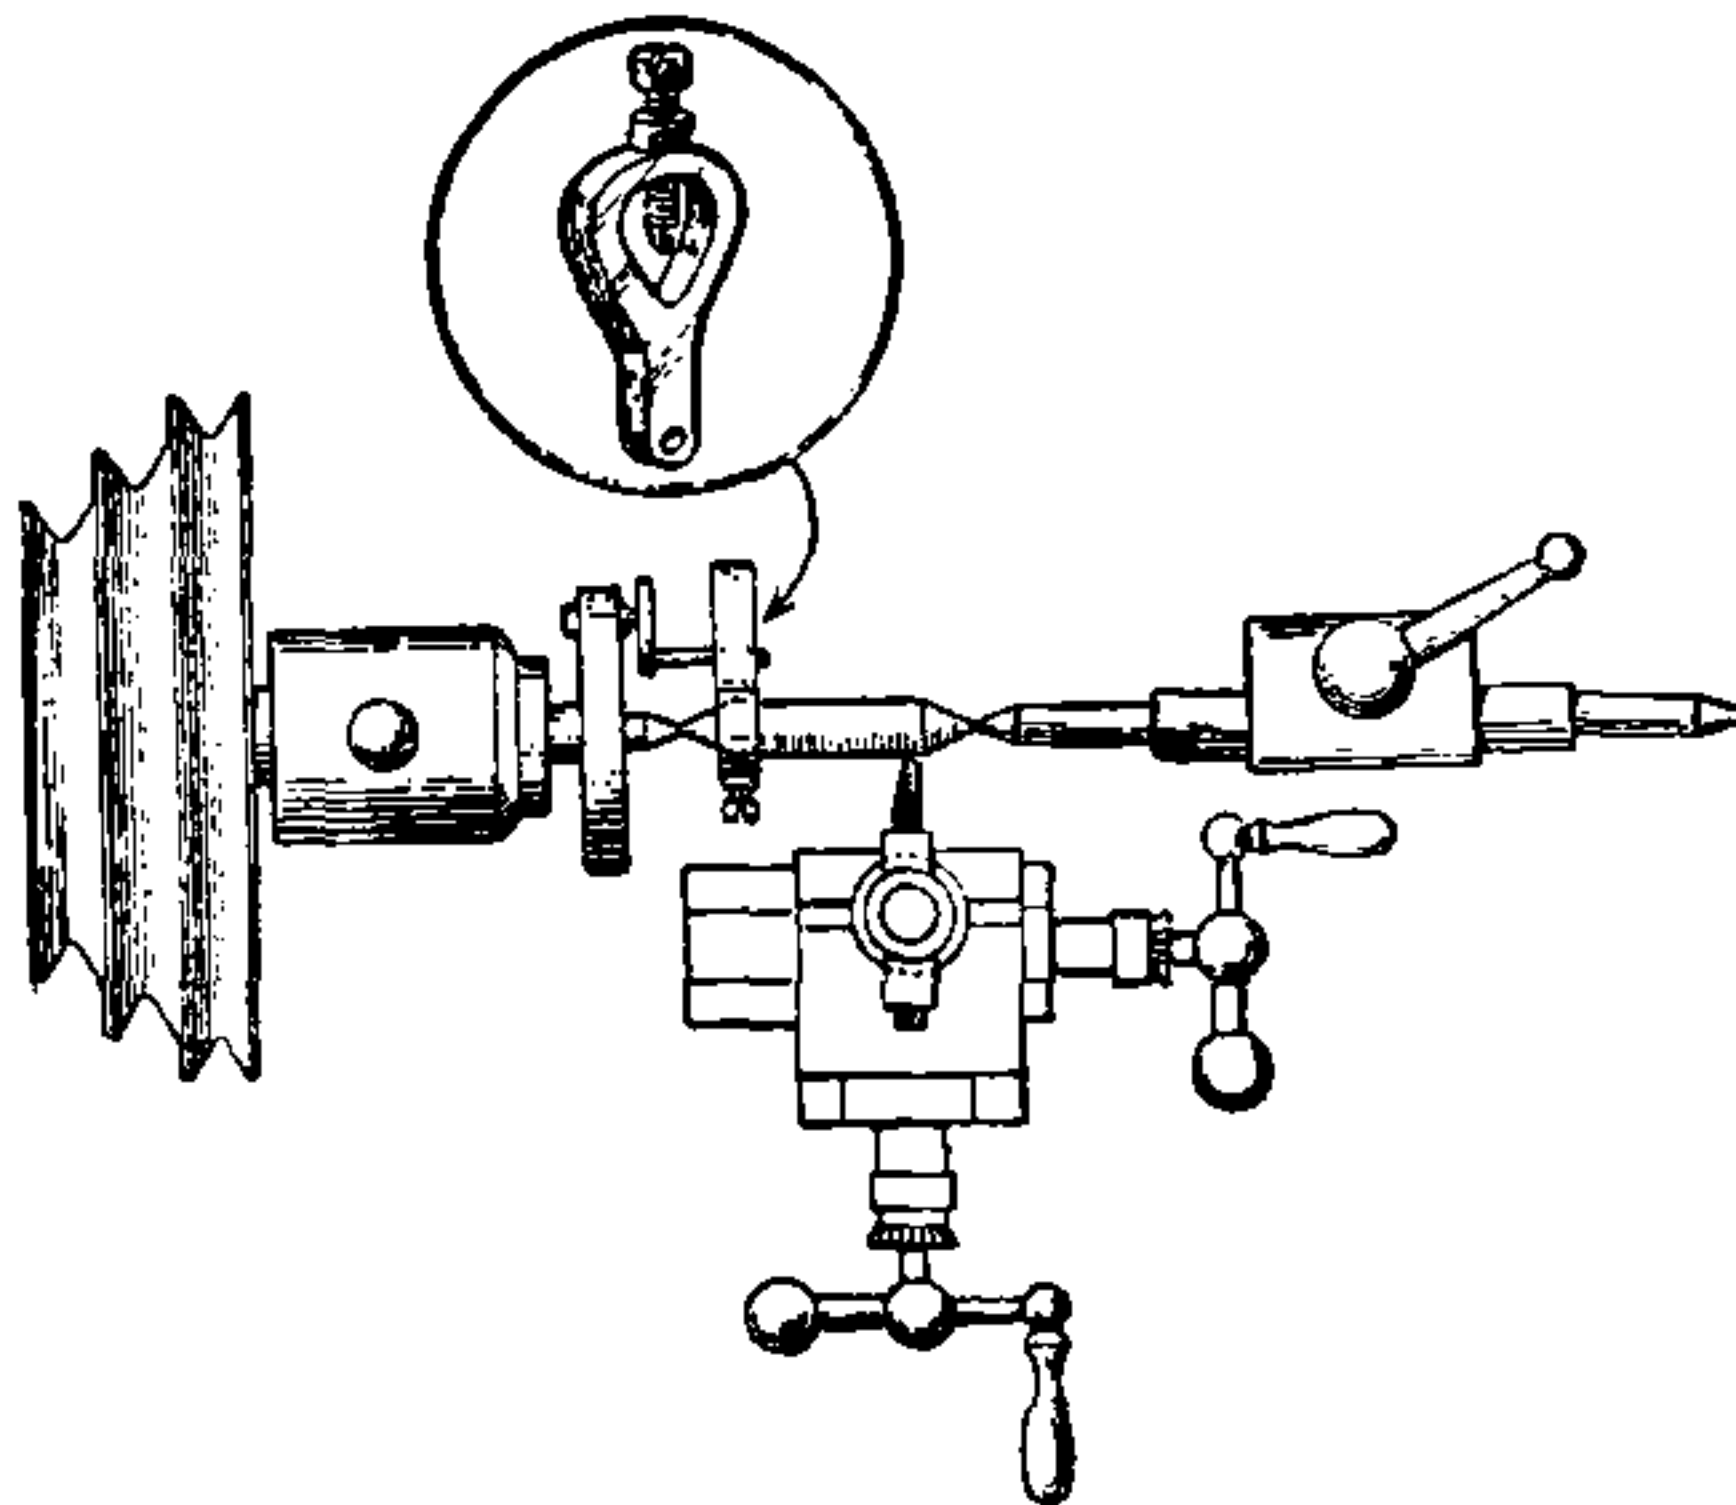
Montaggio per tornire col carrello un pezzo cilindrico.
